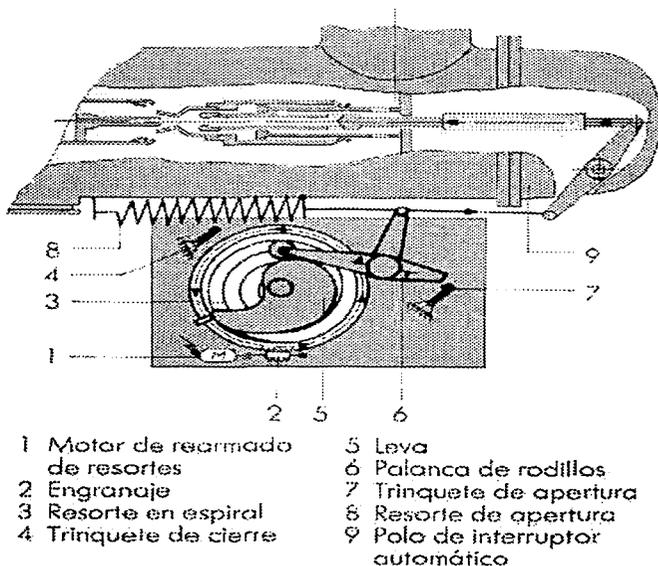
Disposición del Mecanismo de Maniobra.
